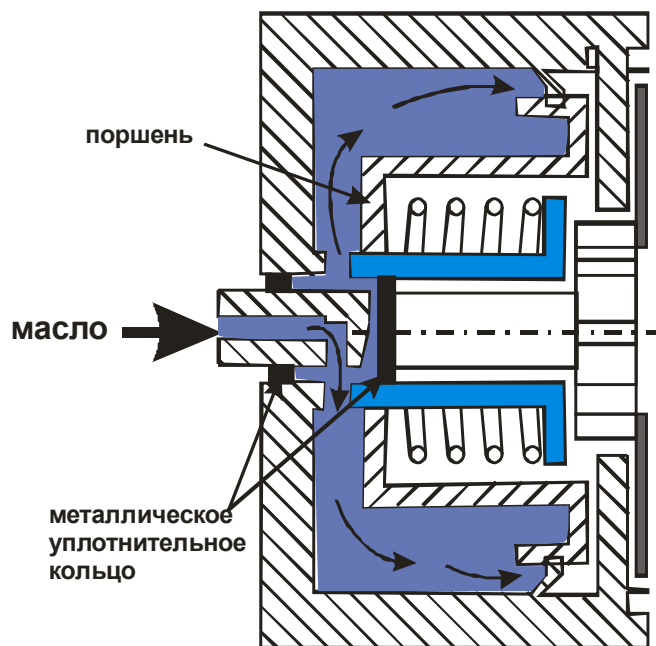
Конструктивная схема автоматической коробки передач с установкой металлических уплотнительных колец.
